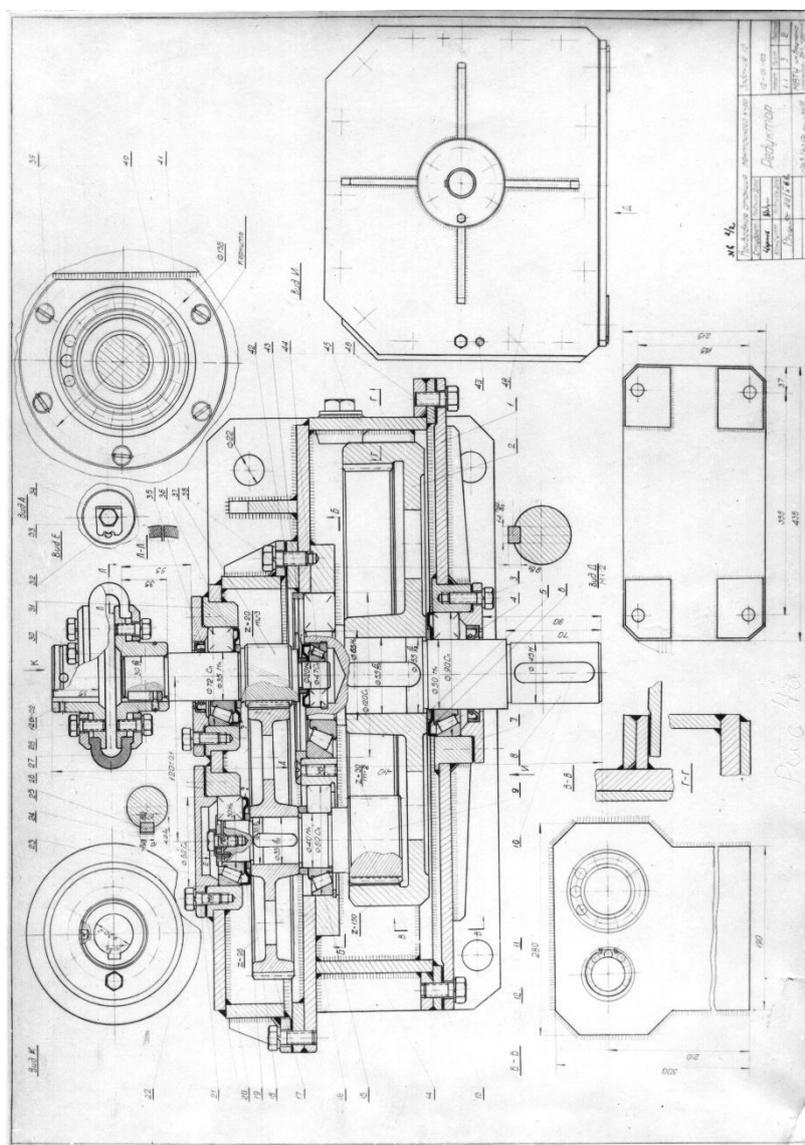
Проекция сборочного чертежа зубчатого соосного редуктора со сварным корпусом (пример)
